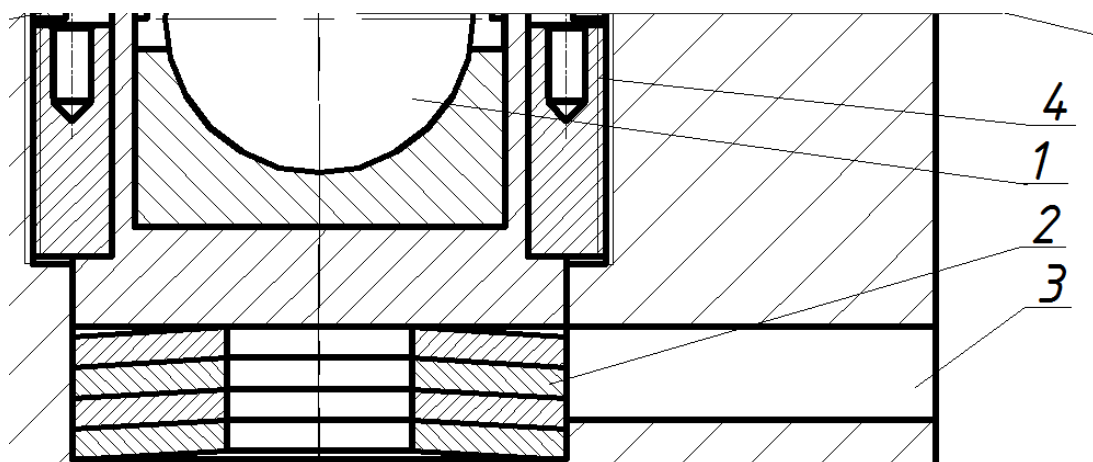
Предохранительное устройство: 1 – шарнир кинематической пары «шатун-ползун»; 2 – пакет тарельчатых пружин, предварительно сжатых до номинальной силы пресса; 3 – фотоэлемент и совмещённое с ним звуковое устройство оповещения; 4 – прижимная резьбовая втулка
